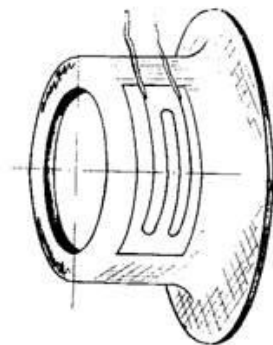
Схема наклеювання тензорезистора на корпус ФД
